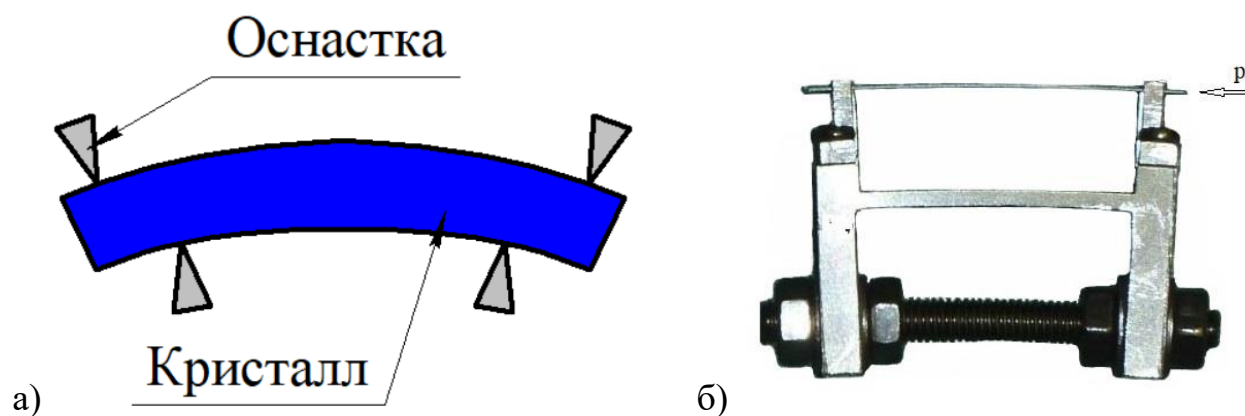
а – схема изгиба, б – внешний вид устройства.
